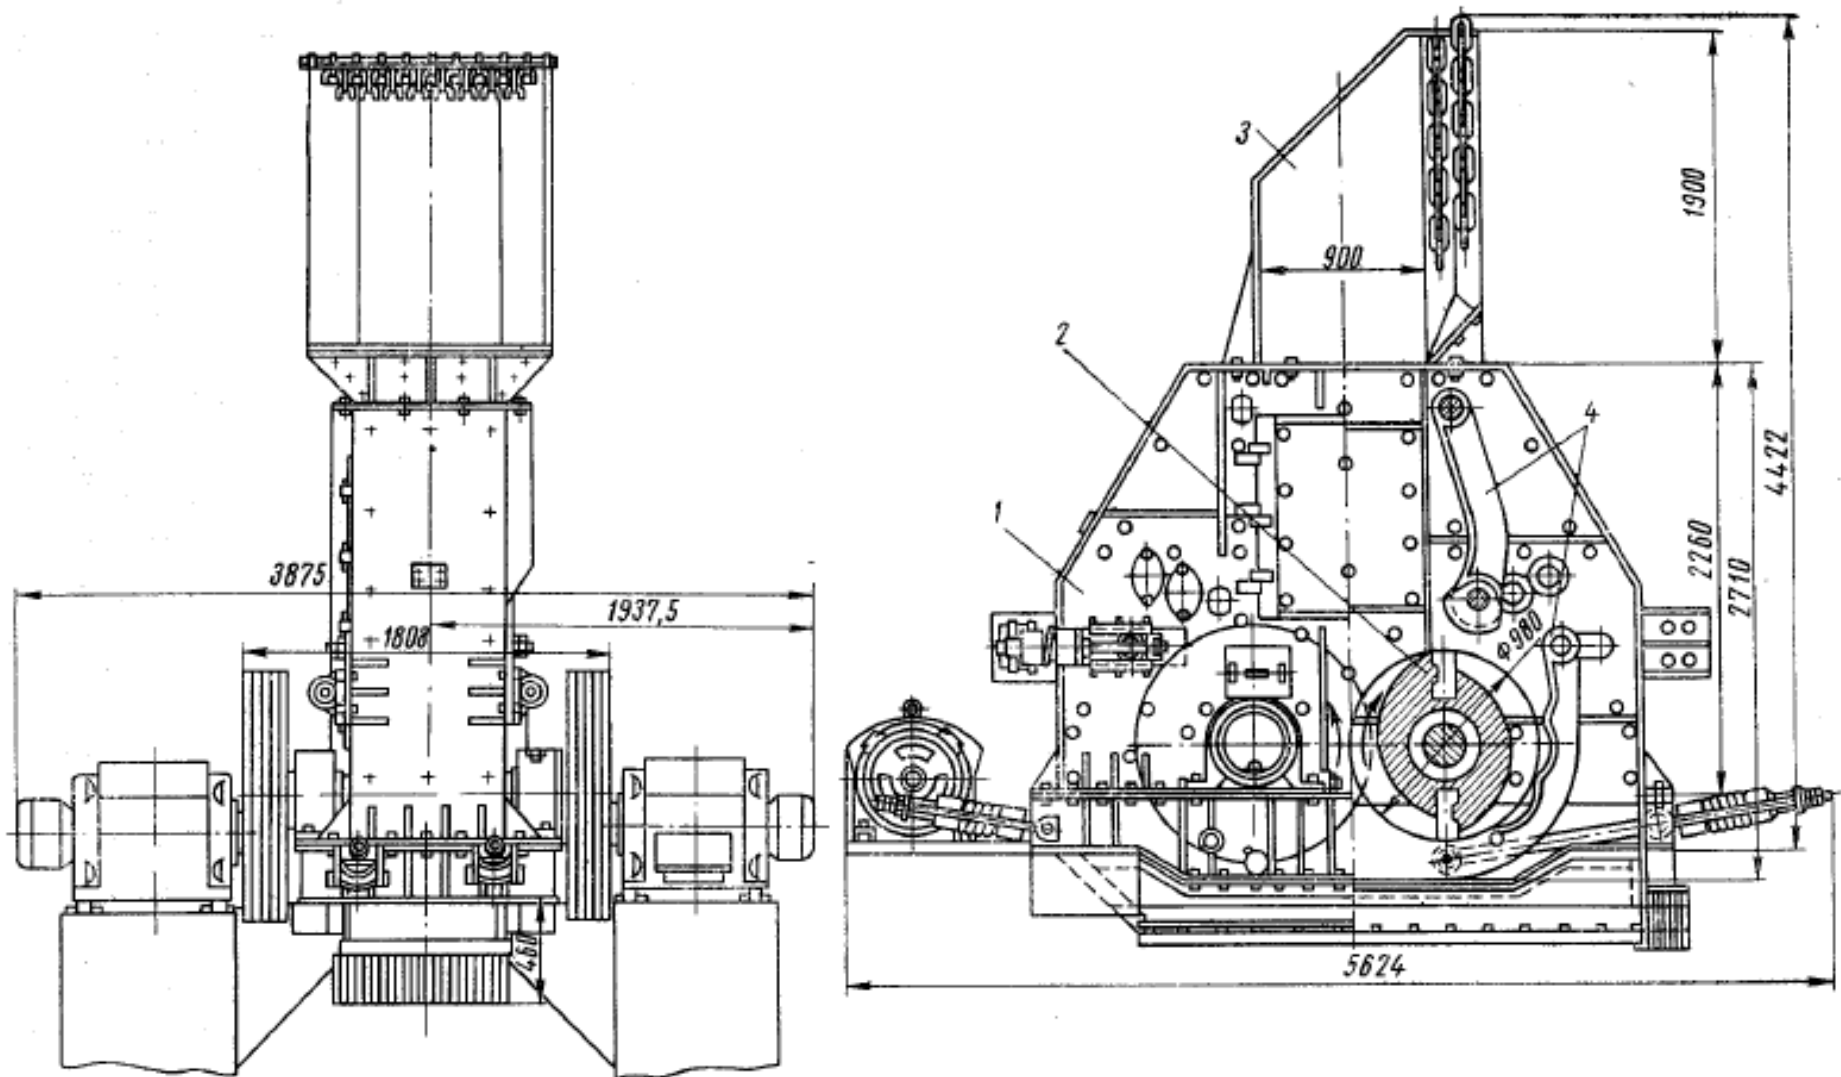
Схема двороторної роторно-бильної дробарки з роторами діаметром 1000 мм:
